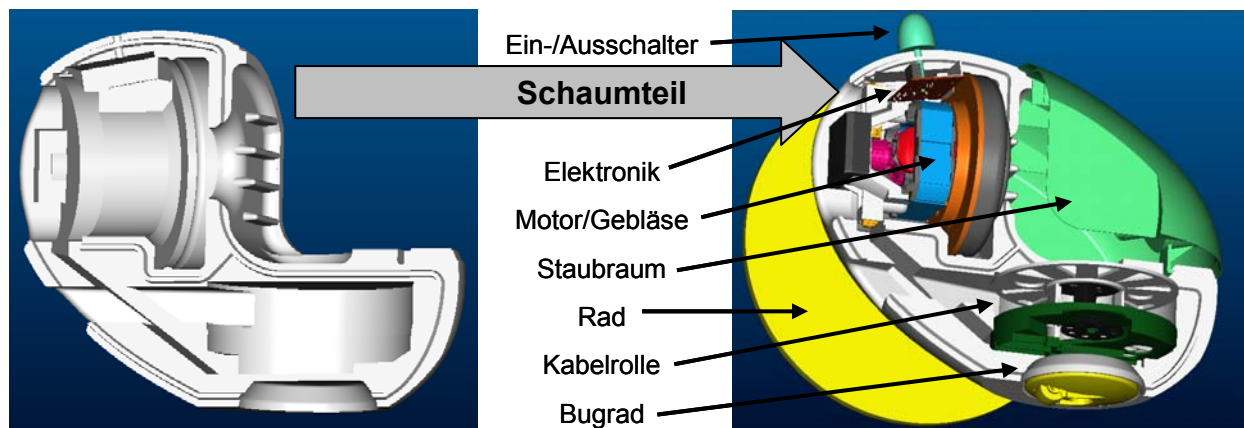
Integration der Komponenten in das Gehäuse aus expandiertem Polypropylen-schaum (EPP) beim Prototypen
